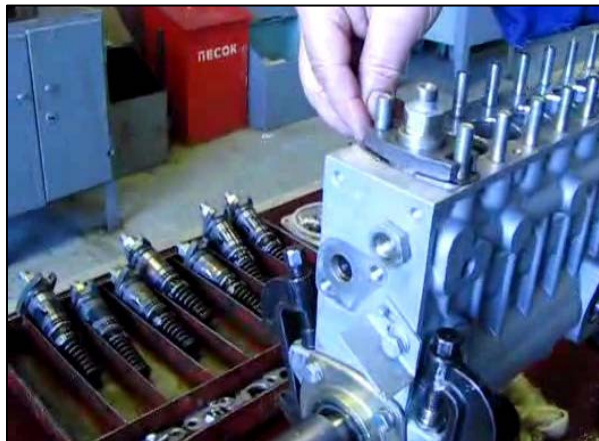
Установка регулировочных прокладок под фланец корпуса секции
